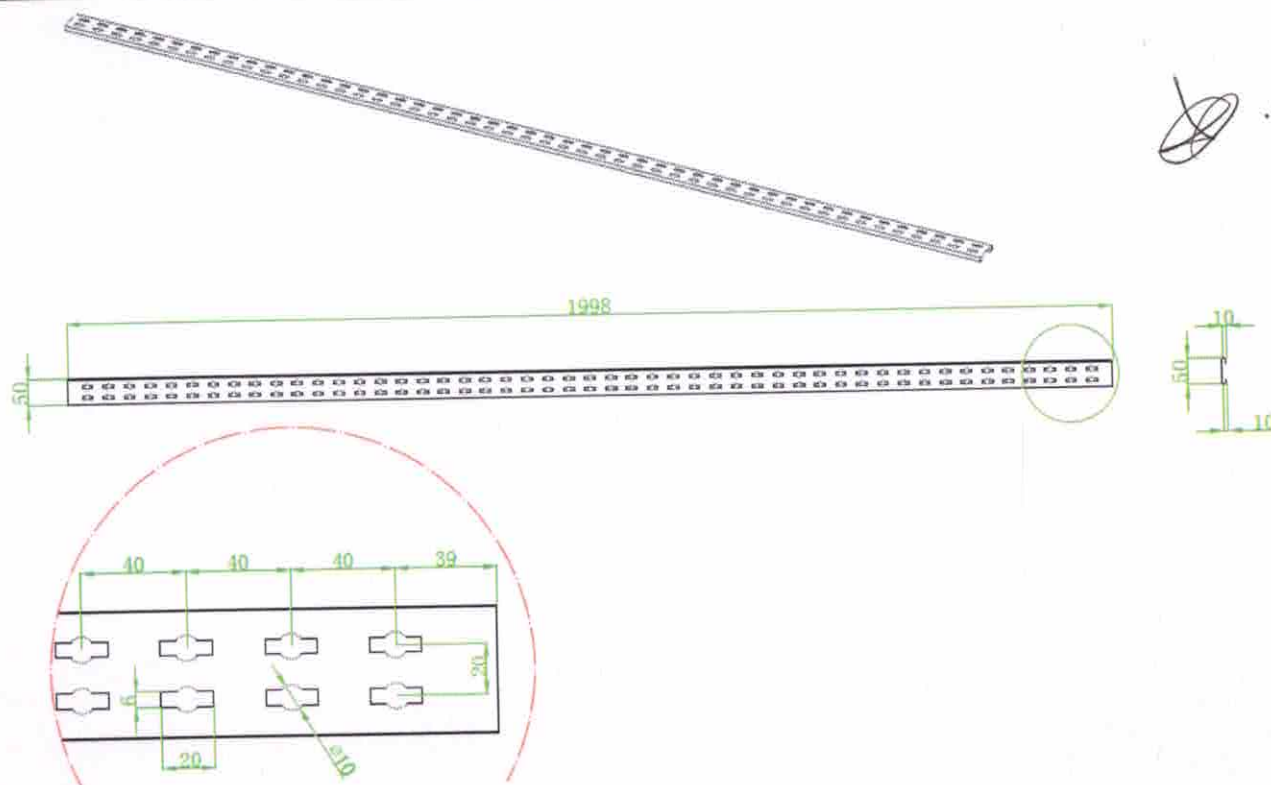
Detalhe do formato das travessas do estrado (medidas em milímetros)
